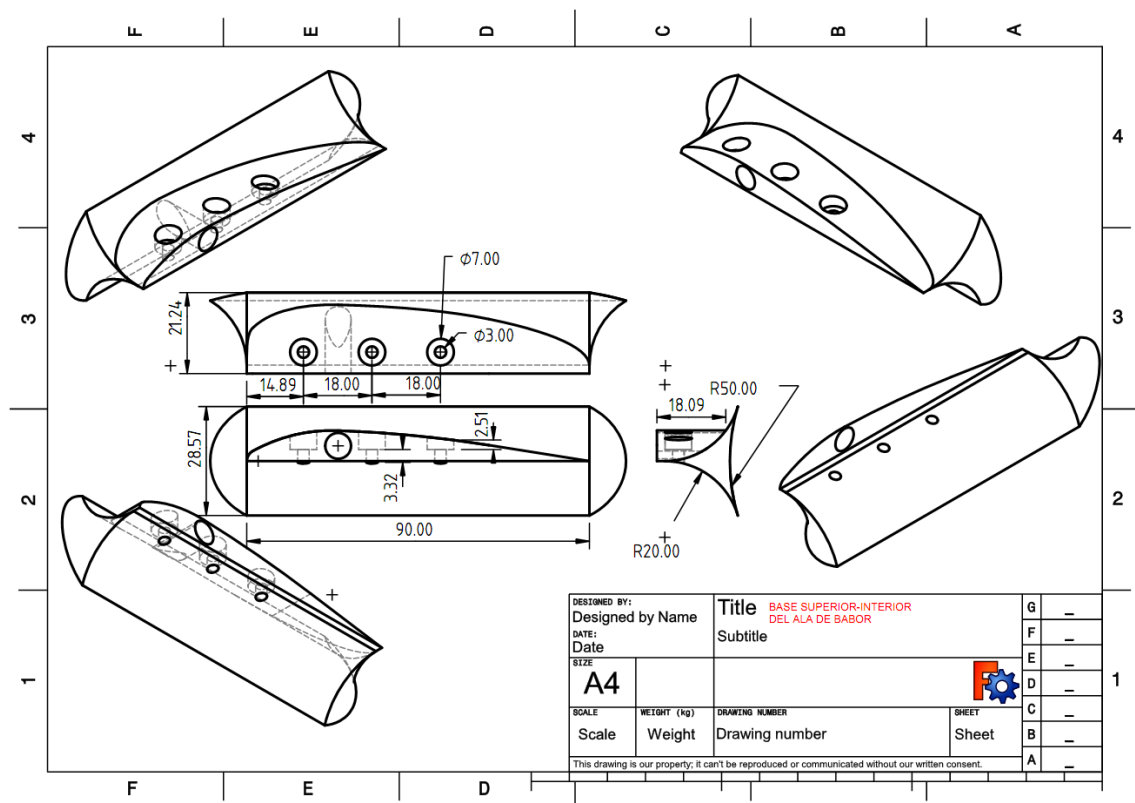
Plano soporte adaptación entre alas y cilindro. Fuente Propia.
